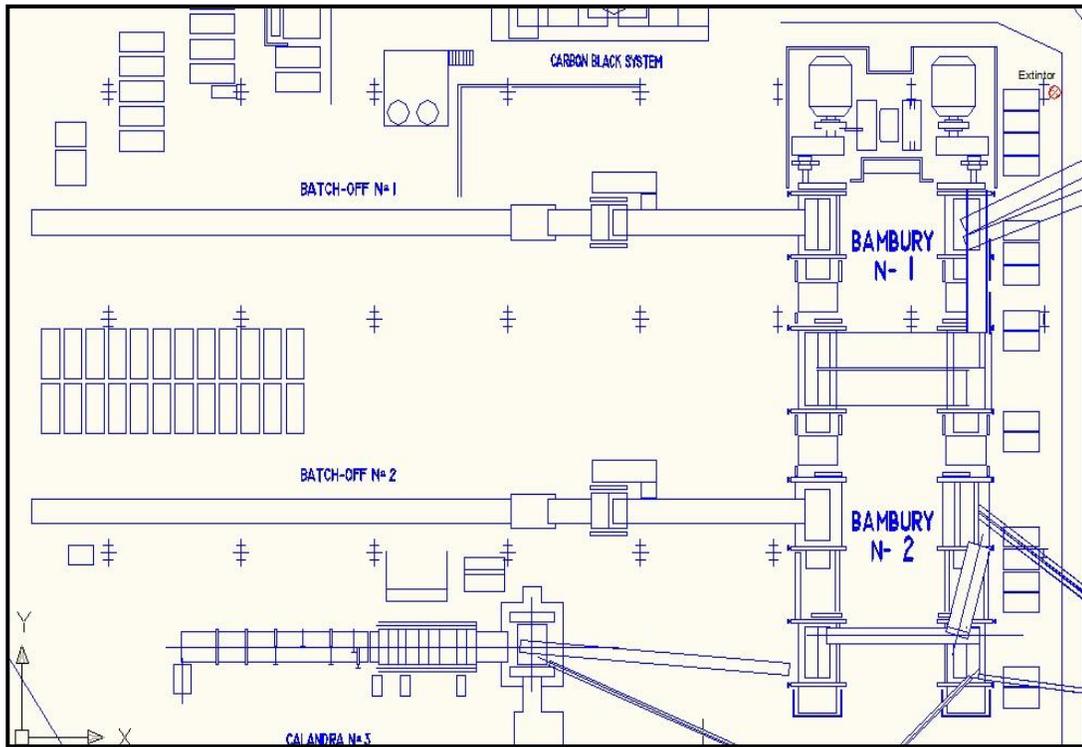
Plano del Departamento de Banbury (1er piso), vista de planta
